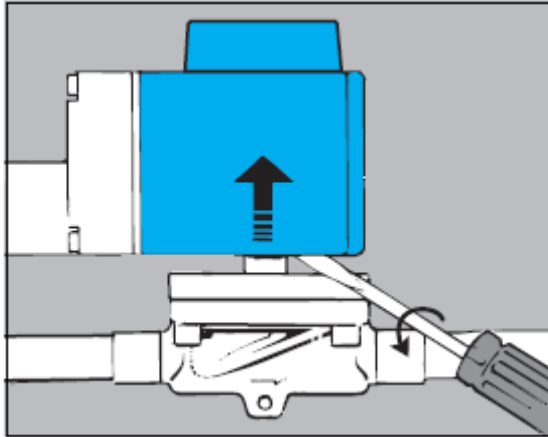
desmontaje de bobina de válvula solenoide.
